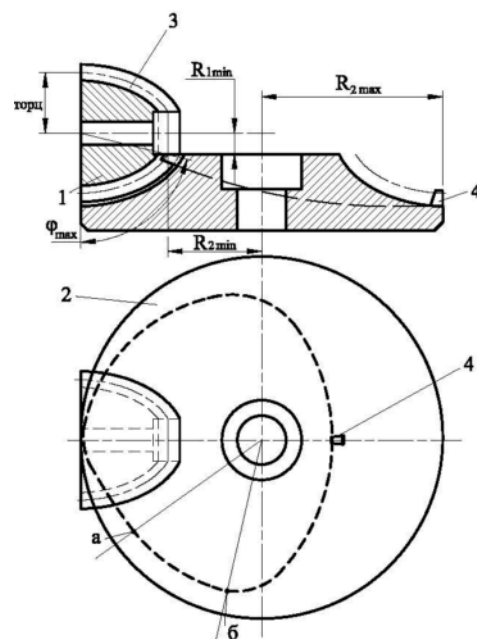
Передача с эллипсоидными и тороидальными колесами
